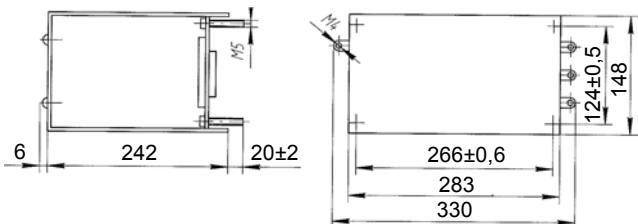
Габаритные, установочные размеры блока типа БЭ 1105.
